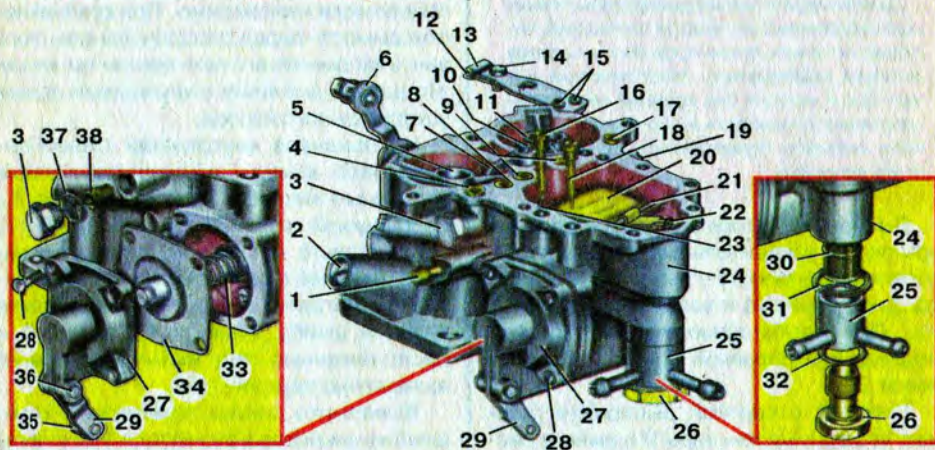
Детали корпуса карбюратора: 1 – штуцер отбора управляющего разрежения для термовакuumного клапана системы рециркуляции отработавших газов; 2 – винт производственной подстройки системы ХХ; 3, 19 – резьбовые пробки; 4 – второй воздушный жиклер системы ХХ; 5, 11 – малые диффузоры первичной и вторичной камер; 6 – рычаг управления пусковым устройством; 7 – распылитель ускорительного насоса; 8 – блок жиклеров системы ХХ; 9 – главные воздушные жиклеры первичной и вторичной камер; 10 – топливоподающий винт крепления распылителя ускорительного насоса; 12 – фиксатор оболочки троса привода воздушной заслонки; 13 – кронштейн троса привода воздушной заслонки; 14, 15, 28 – винты; 16 – ограничитель хода всасывающего клапана ускорительного насоса; 17 – воздушный жиклер переходной системы вторичной камеры; 18 – винт регулировки подачи ускорительного насоса; 20 – поплавок; 21 – ось поплавка; 22 – топливный клапан; 23 – шарик всасывающего клапана ускорительного насоса; 24 – корпус карбюратора; 25 – блок штуцеров подвода и слива топлива; 26 – топливоподающий винт; 27 – крышка ускорительного насоса; 29 – рычаг привода ускорительного насоса; 30 – топливный фильтр; 31, 32, 37 – уплотнительные шайбы; 33 – возвратная пружина диафрагмы ускорительного насоса; 34 – диафрагма ускорительного насоса; 35 – ролик рычага привода ускорительного насоса; 36 – ось рычага привода ускорительного насоса; 38 – эмульсионный жиклер системы ХХ
